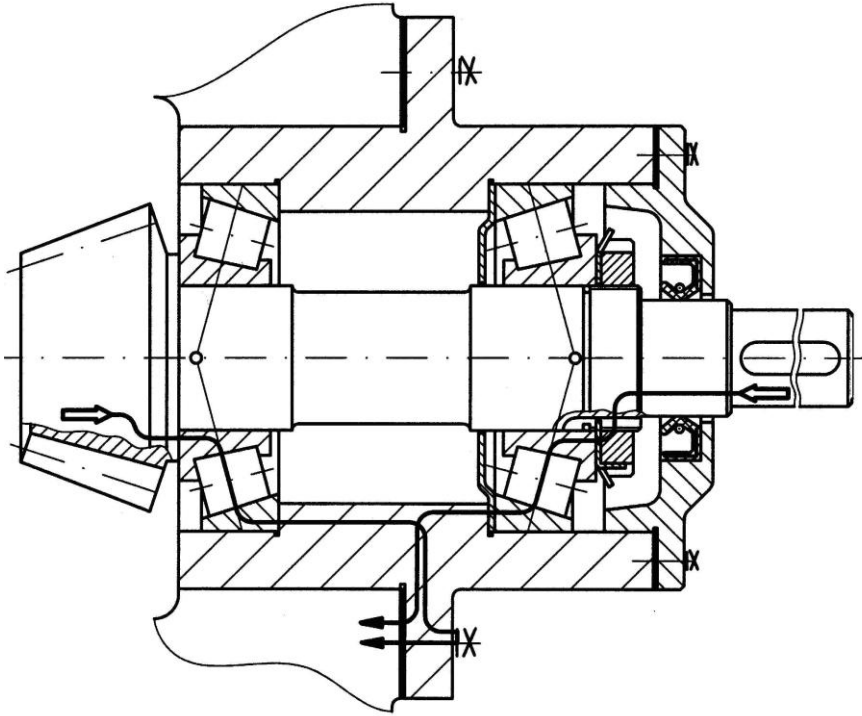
Montaj cu fixare axială la ambele capete, în “O”,
